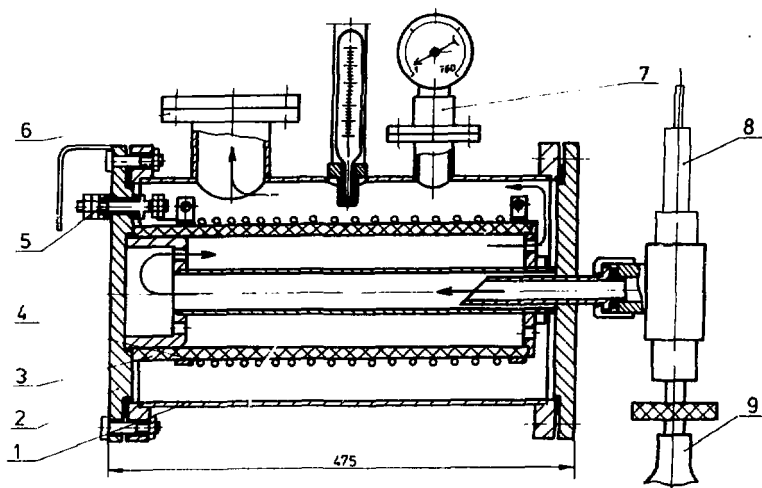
Система напуска сухого азота: 1 - корпус; 2 - крышка корпуса; 3 - труба керамическая; 4 - нагреватель; 5 - электроввод; 6 - фланец клапана напуска; 7 - мановакуумметр; 8 - предохранительный клапан; 9 - сосуд Дьюара.
